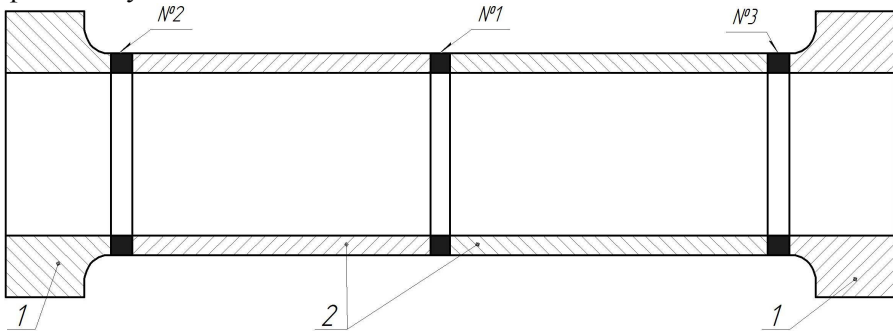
Зварні з’єднання станин важких пресів
